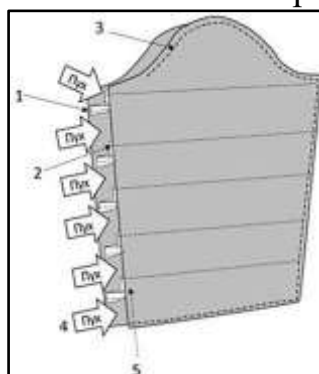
Схема пухового пакета и отверстий для набивки пухом с переборками
